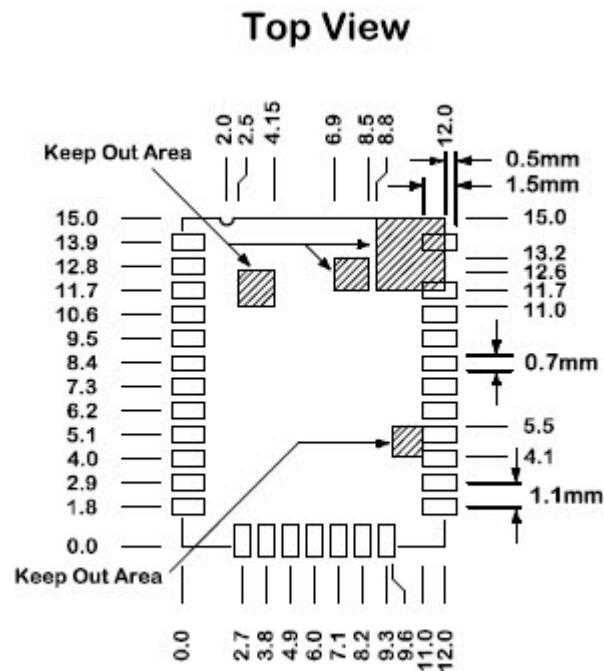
建议的 BM70BLE01FC2 PCB 尺寸
